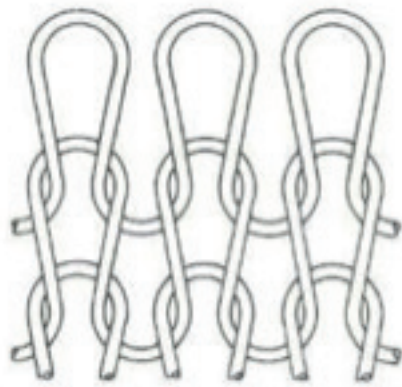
Vista de elementos entretreídos que constituyen el género de punto
